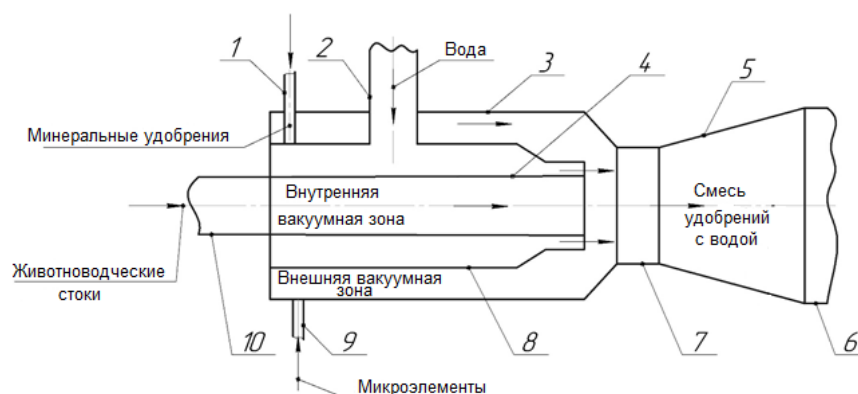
Схема кольцевого двухповерхностного струйного смесителя
